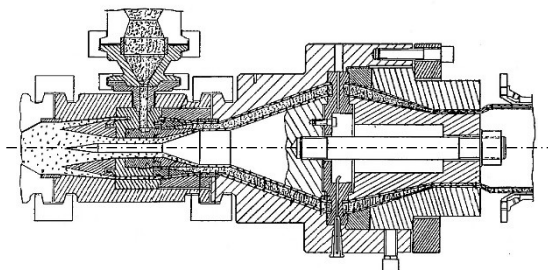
Головка для формування тришарової трубчастої заготовки (пат. № US4364882A)
